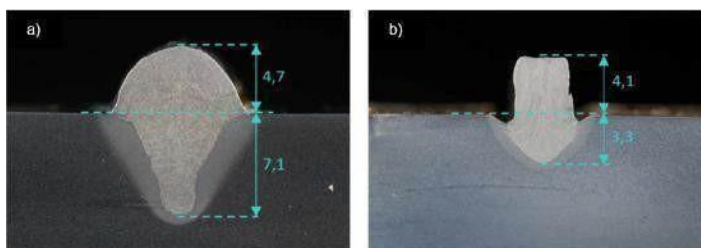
Macrografias. Fonte: O autor. Em a) Cordão de solda D1, $V_c = 0,6$ m/min; b) Cordão de solda D12, $V_c = 1,7$.
